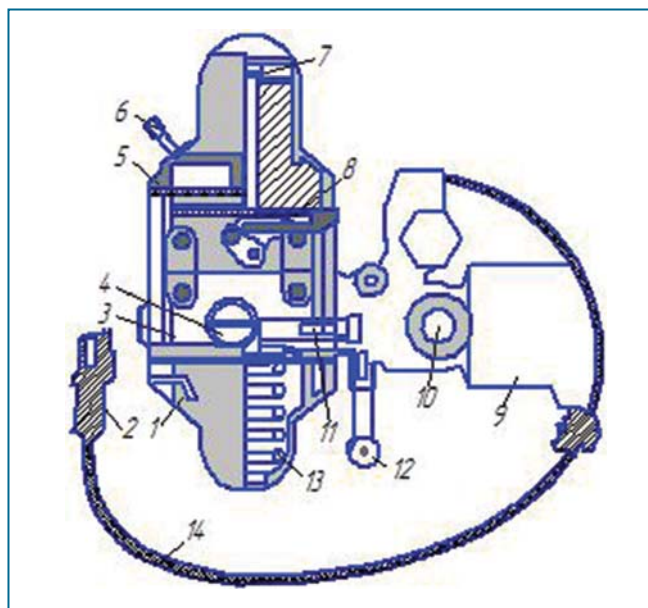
Редуктор высокого давления для КПГ фирмы Landi Renzo CNGNG 2–3 КПГ: 1 – крышка; 2 – штекер; 3 – первая ступень; 4 – предохранительный клапан; 5 – ступень низкого давления; 6 – штуцер вакуумной коррекции редуктора; 7 – винт регулировочный первой ступени; 8 – датчик давления газа; 9 – электромагнитный клапан; 10 – штуцер подачи газа; 11 – ступень высокого давления; 12 – штуцер; 13 – пружина; 14 – жгут проводов
